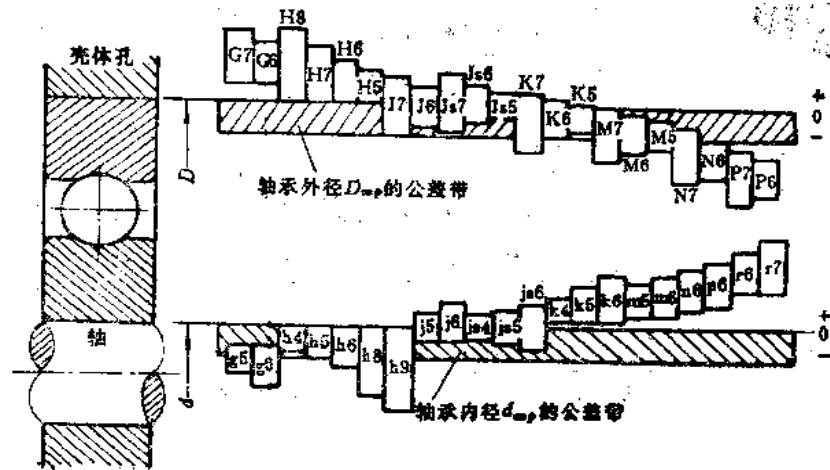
滚动轴承与轴和孔的公差与配合
